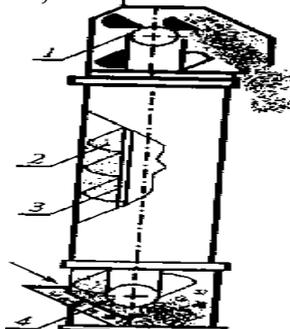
Схемы нории с центробежной разгрузкой: 1 - приводные звездочки- 2 - ковши 3 - тяговые органы; 4 - натяжная звездочка
